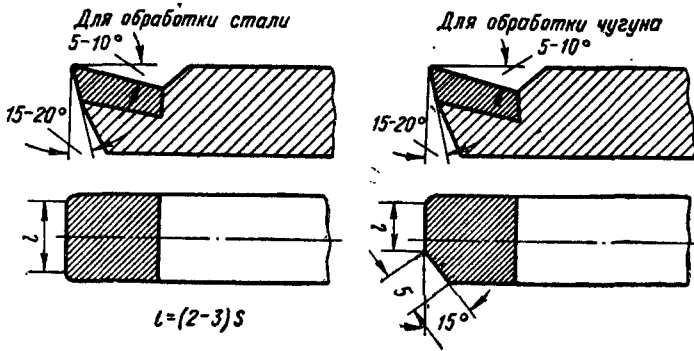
Форма и геометрические параметры широких резцов для чистового обтачивания.
